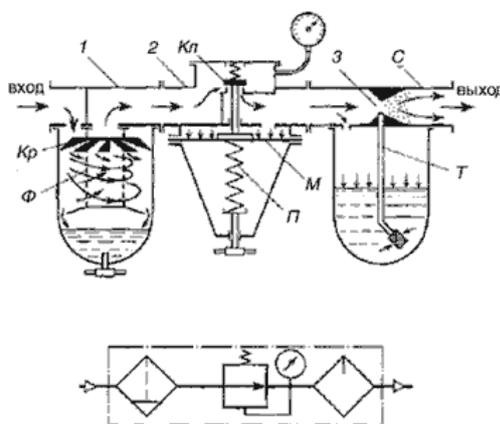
Типовой узел подготовки воздуха: а - принципиальная схема; б - условное обозначение
